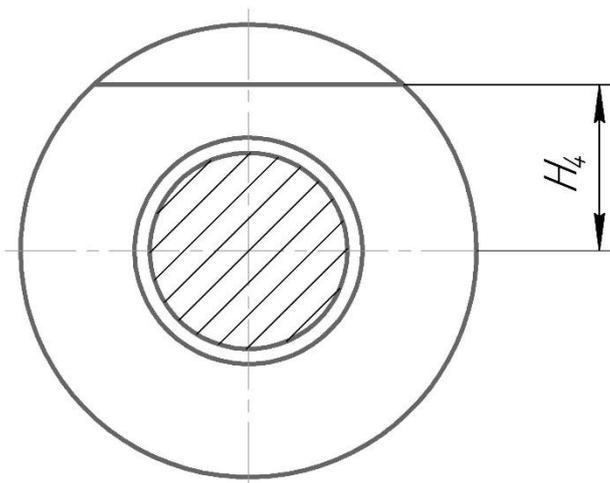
Схема для расчета погрешности базирования при креплении детали на разжимную оправку
